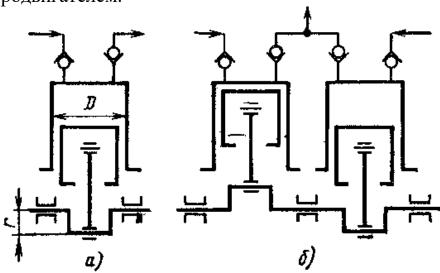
Схемы одноступенчатого (a) и двухступенчатого (б) компрессоров с рядным расположением цилиндров
